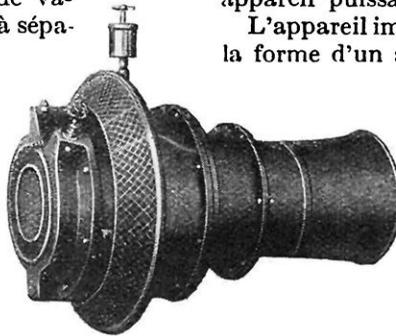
TURBINE SOUFFLANTE A VANNE DIRECTRICE DE M. F. COPPUS
